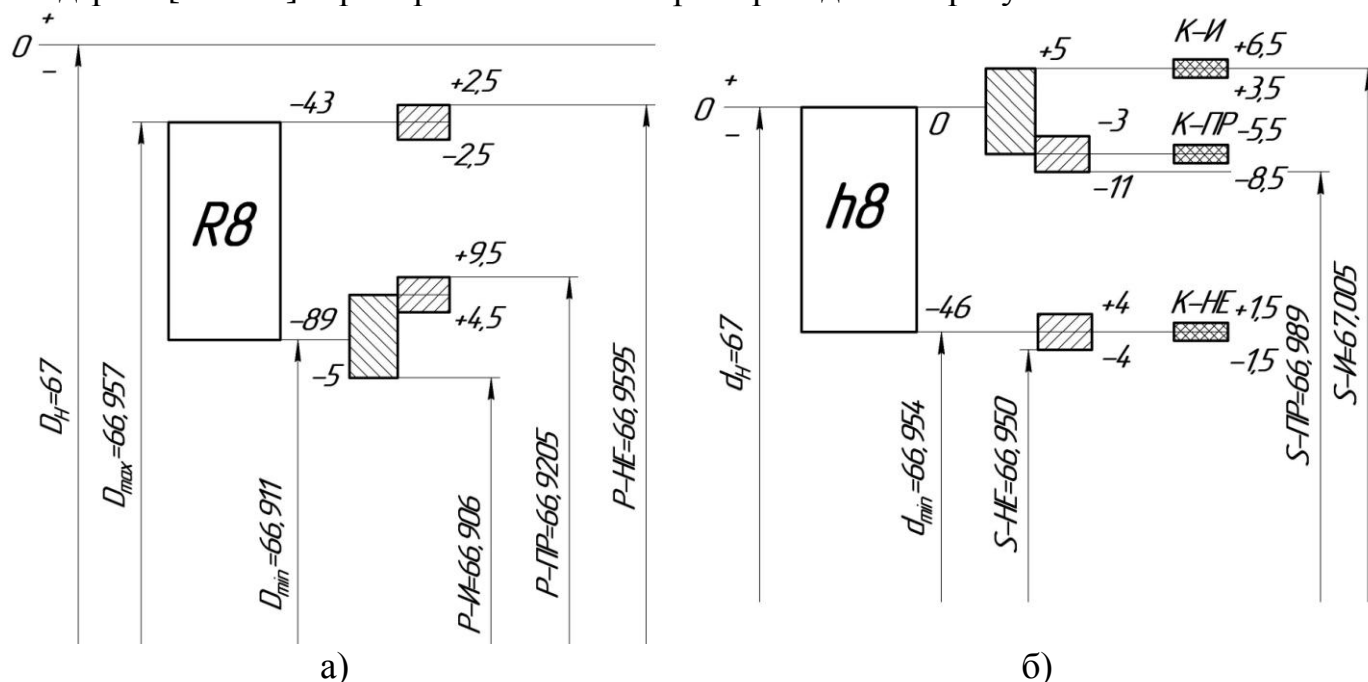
Схемы расположения полей допусков калибров:
